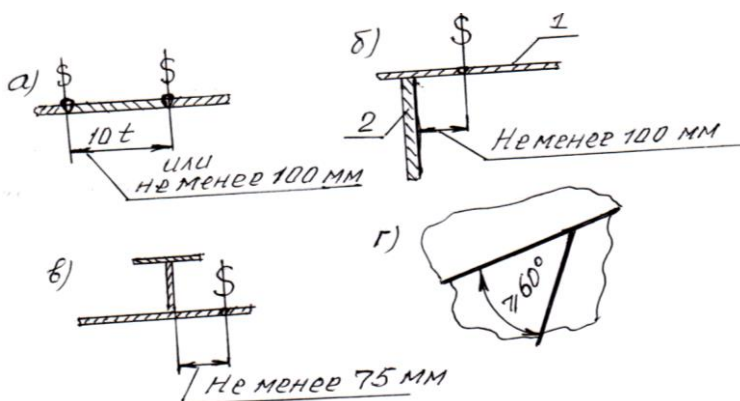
Требования «Правил Регистра» к взаимному расположению сварных швов:
